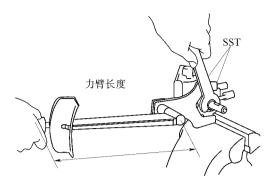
安装小齿轮轴承调整螺钉锁紧螺母
